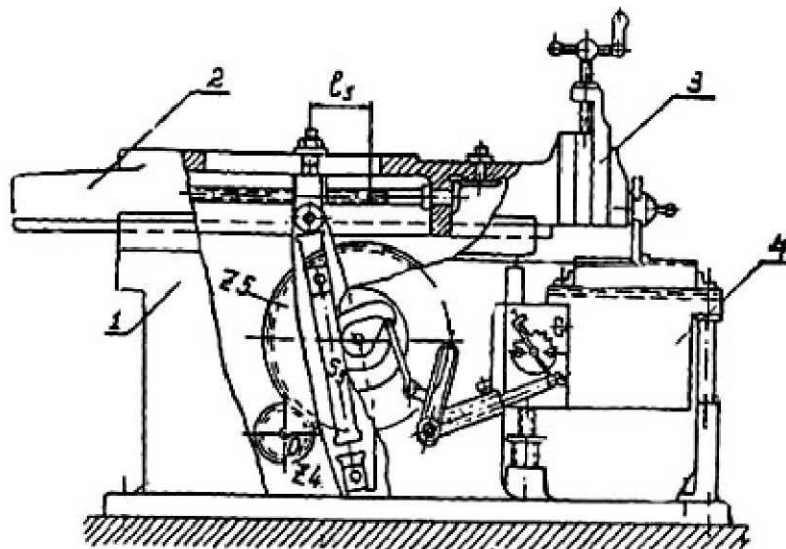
Общий вид поперечно-строгального станка с качающейся кулисой
